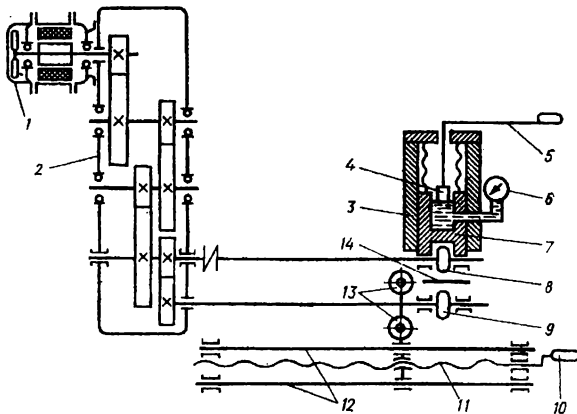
Кинематическая схема пиловальцовочного станка:
